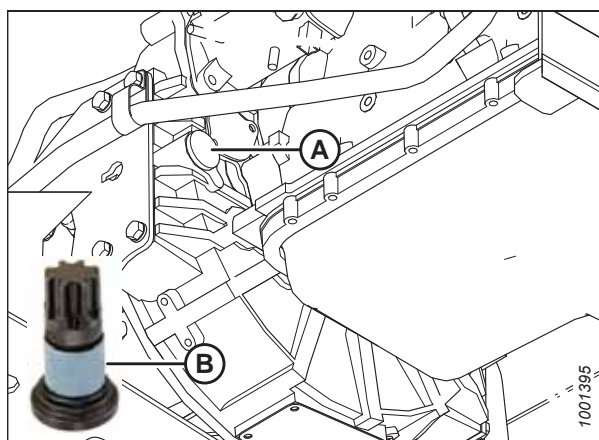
Расположение отверстия для инструмента для проворачивания коленвала
